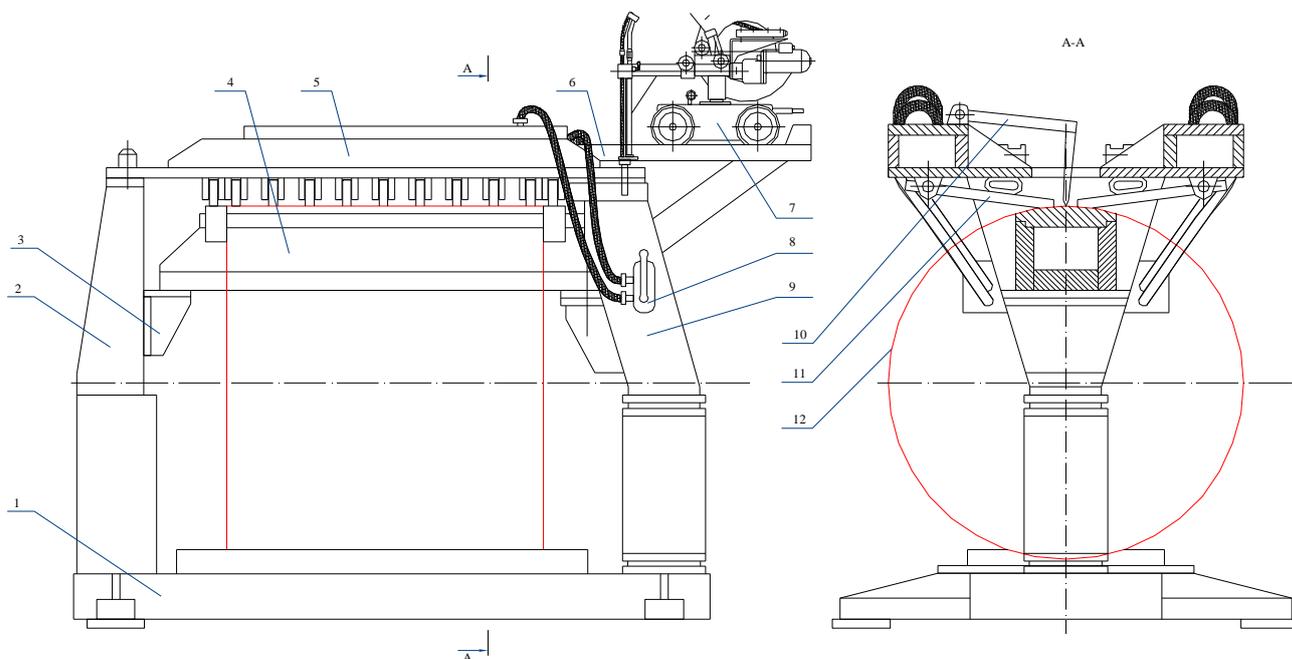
Установка для сварки продольного шва обечайки.
